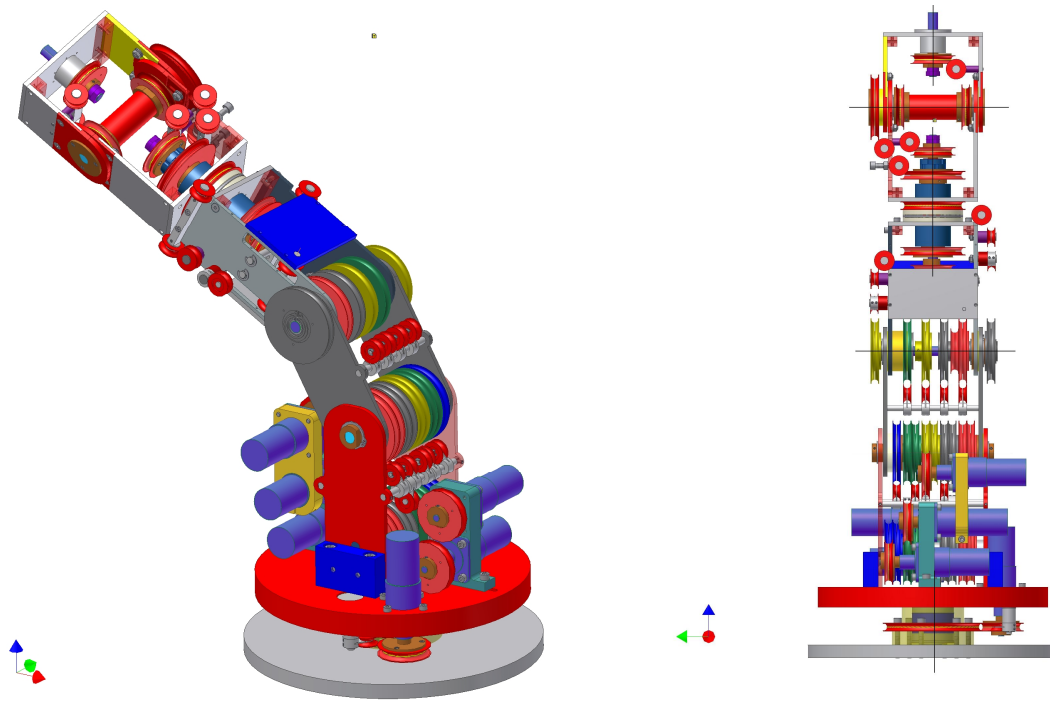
Ingeniería de detalle vistas frontal + perspectiva
